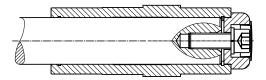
riduttore fissato ad un albero senza spallamento mediante elemento di fissaggio
